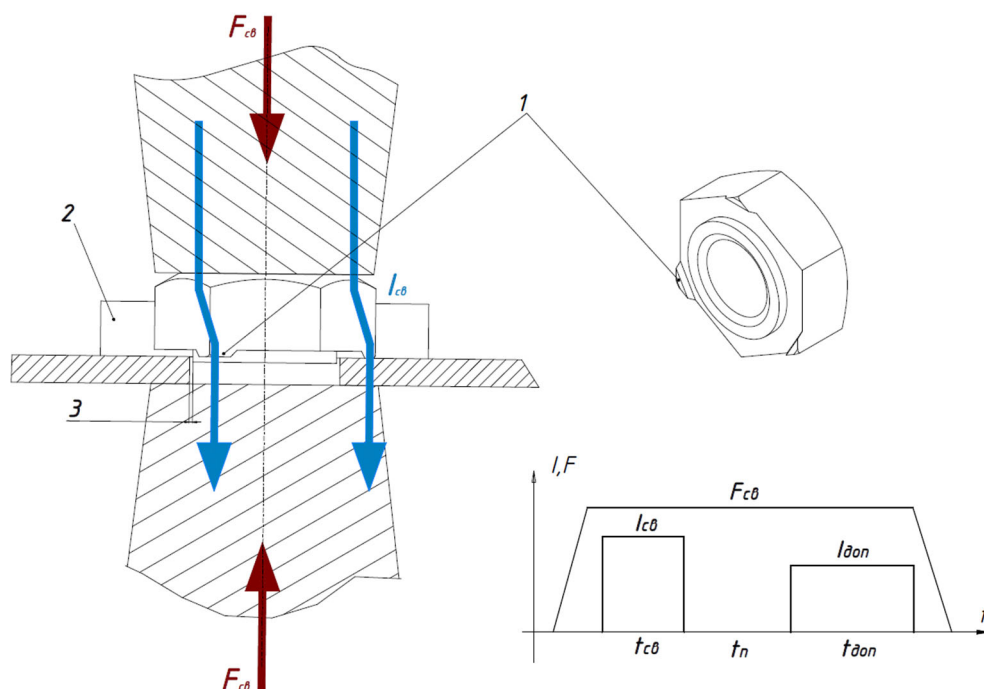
Процесс рельефной сварки. 1-рельефный выступ, 2-фиксатор, 3-зазор 0,25мм.
